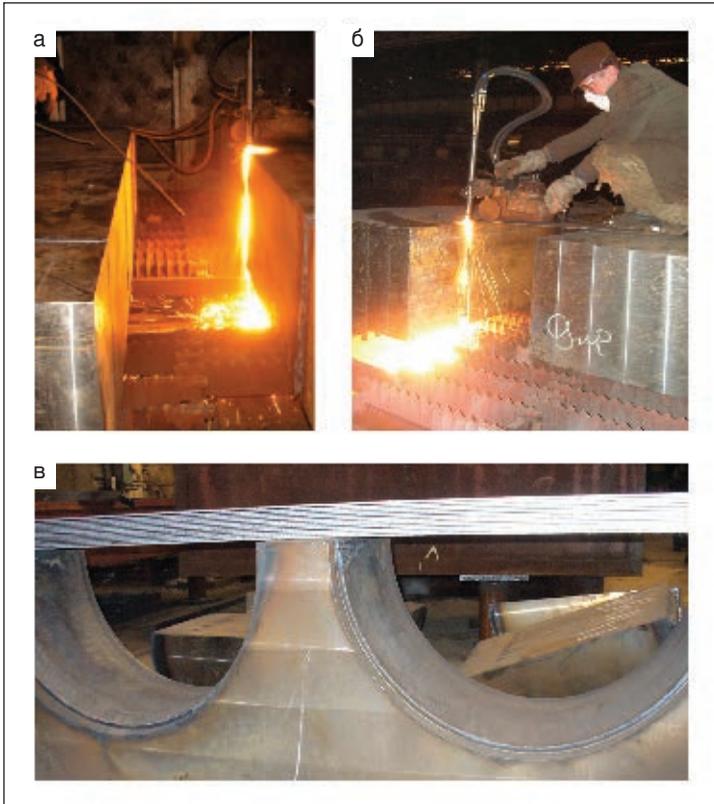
Вырезка отверстий диаметром 800 мм резаком TORH-M на заготовках корпуса подшипника толщиной 450 мм, сталь 40X: а — врезание; б — окончание резки; в — поверхность реза. Мундштук №4, диаметр режущего канала 4,5 мм
